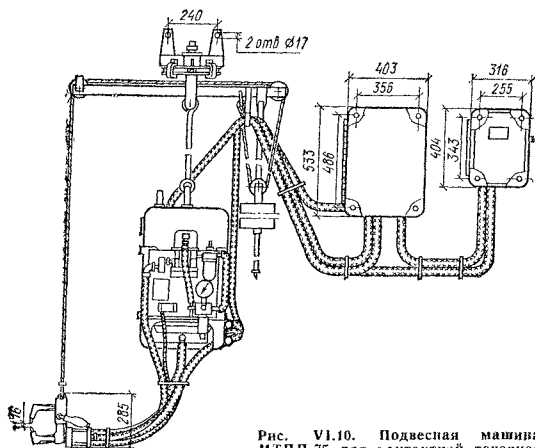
Подвесная машина МТПП-75 для контактной точечной сварки с клещами КТП-2
